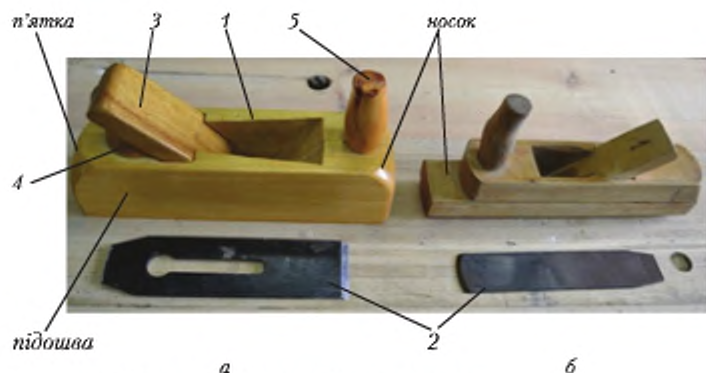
Будова рубанка (а) і шерхбеля (б)
